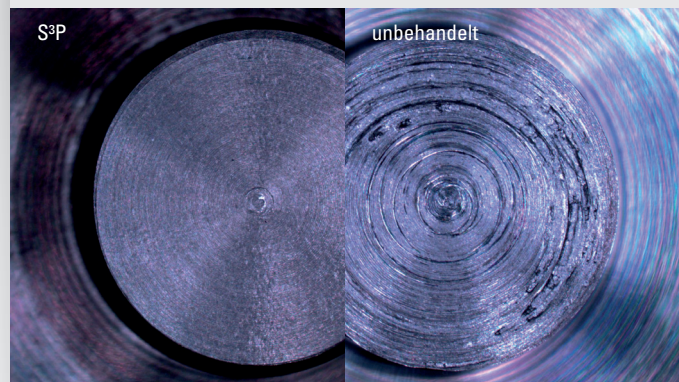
Abbildungen von zwei AISI 316 Bolzen nach der G98-Prüfung auf Kaltverschweißen. Links: Zustand nach der S³P Behandlung bei 842,5 MPa (122,2 KSI), kein Kaltverschweißen; Rechts: unbehandelter Zustand bei 45,5 MPa (6,6 KSI), Kaltverschweißen.
